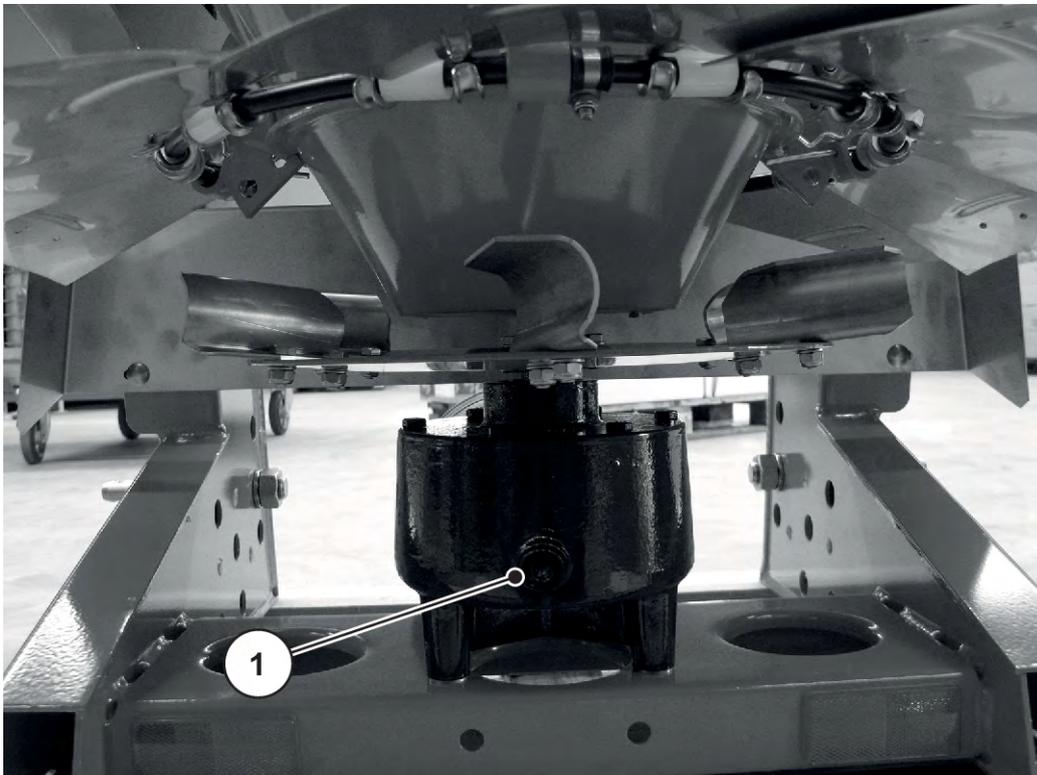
Kontrollschraube Ölstand Getriebeöl
